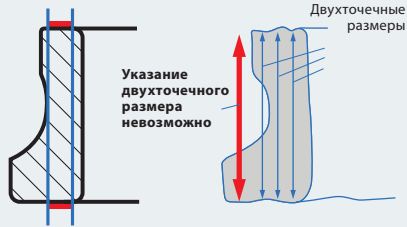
Пример указания допуска ширины внутреннего кольца радиально-упорного шарикоподшипника.
